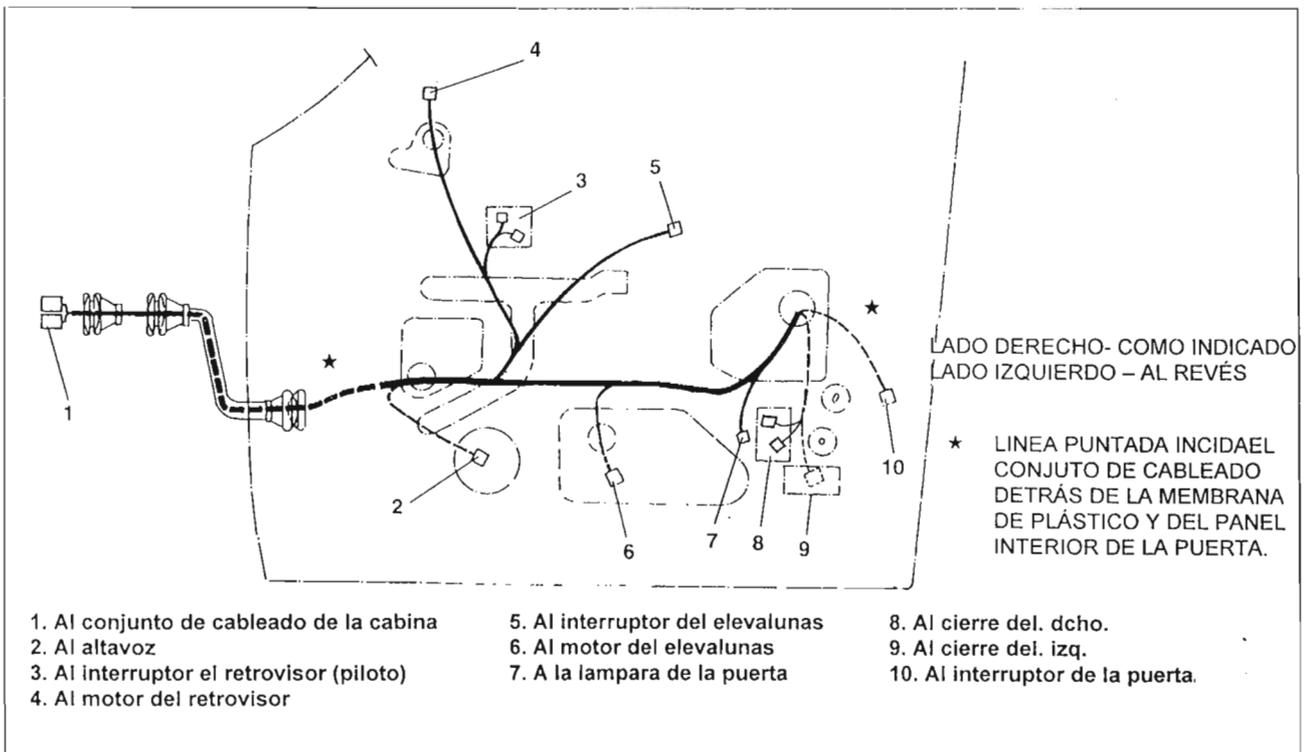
Conjuntos de cableado de la puerta delantera izquierda / derecha
